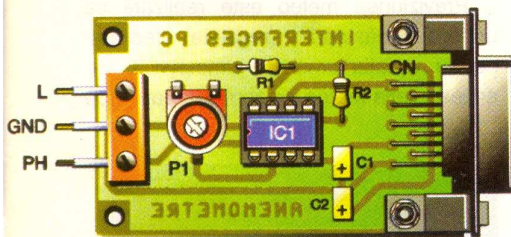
Interfața PC, vedere dinspre față echipată cu componente
